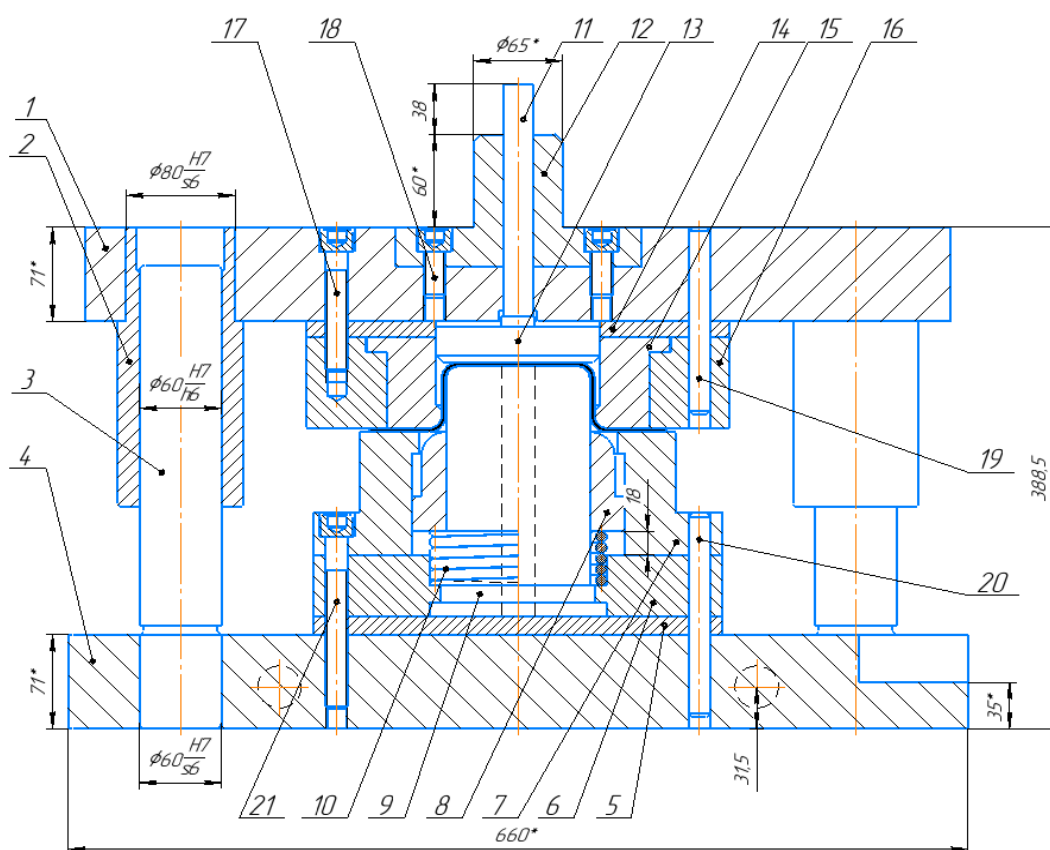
Общий вид штампа для второй и третьей вытяжек:
